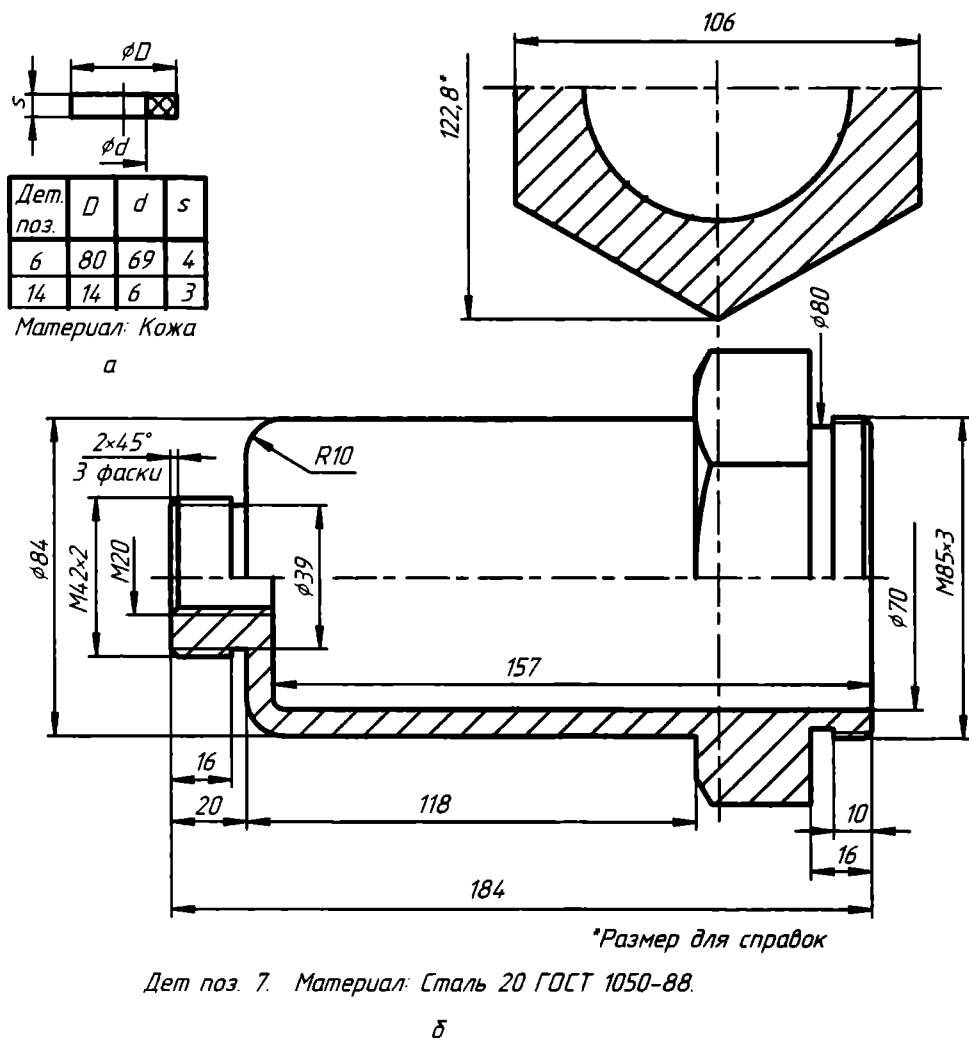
Чертежи: а — прокладок; б — цилиндра
